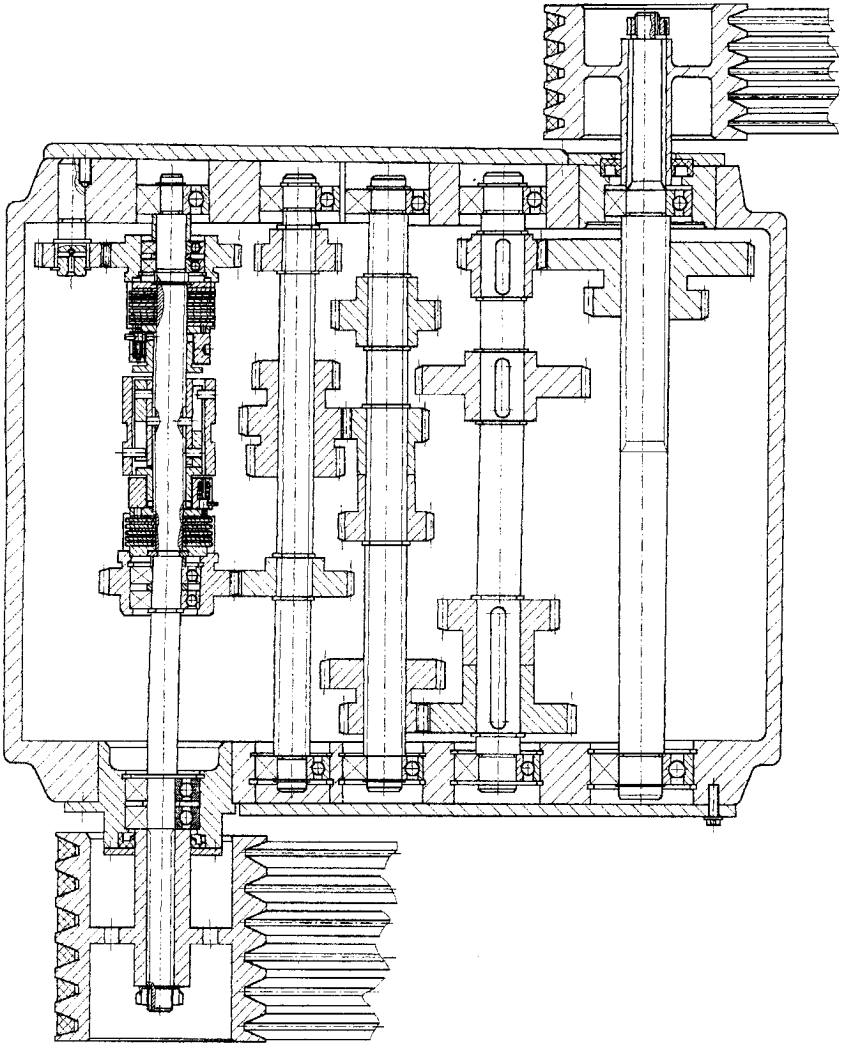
Розгортка поздовжнього перерізу коробки швидкостей токарного та токарно-револьверного верстатів
